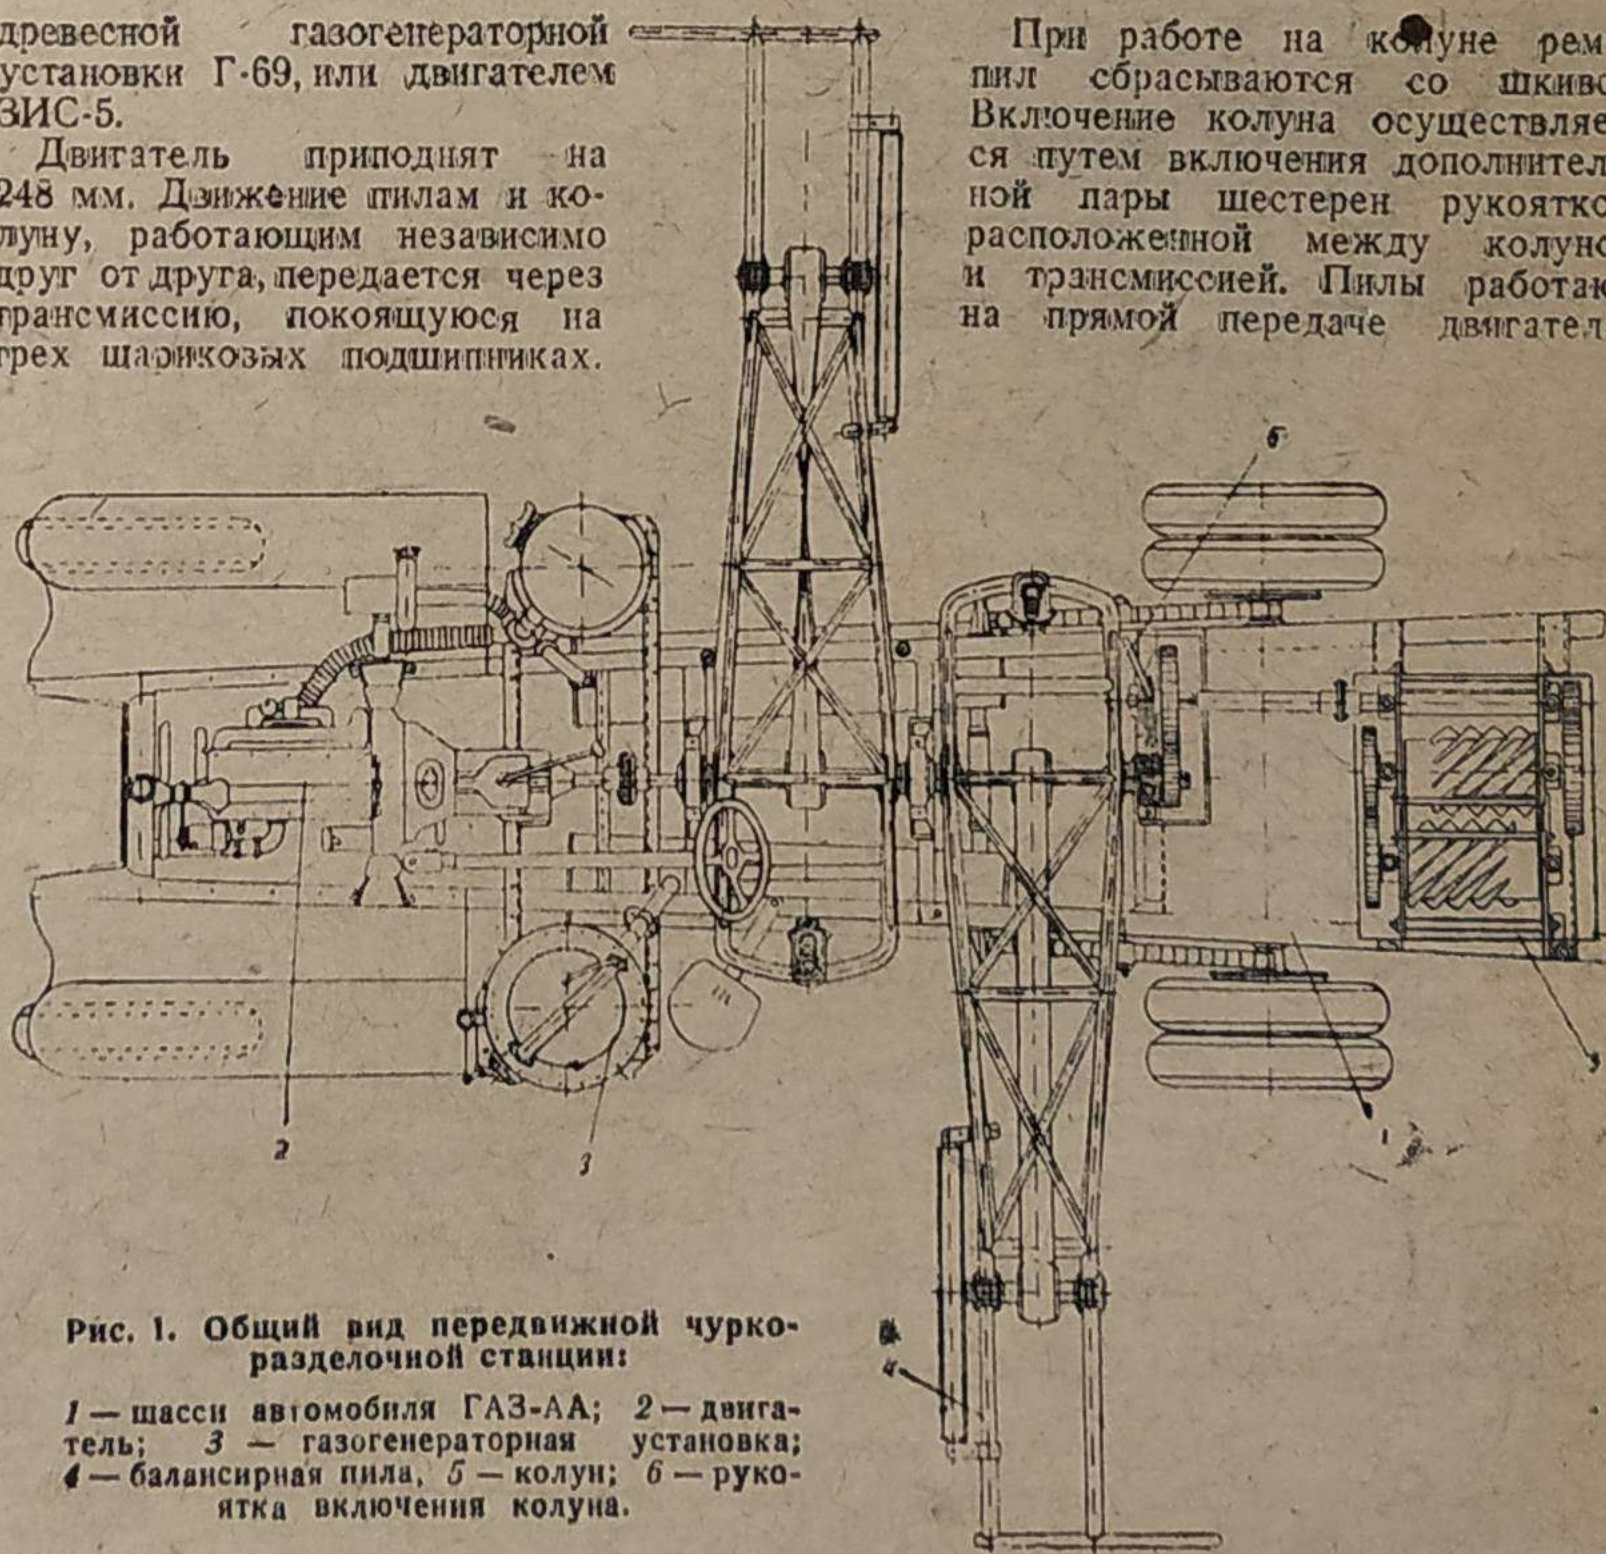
Общий вид передвижной чуркоразделочной станции:
